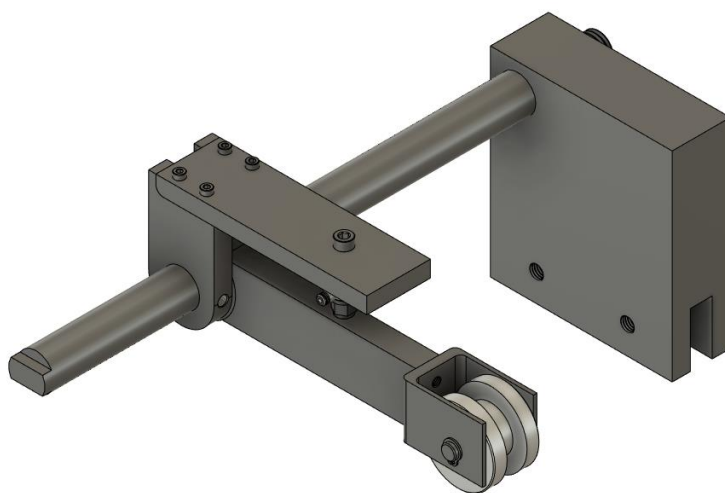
Assemblagem de todos os componentes do protótipo final.
